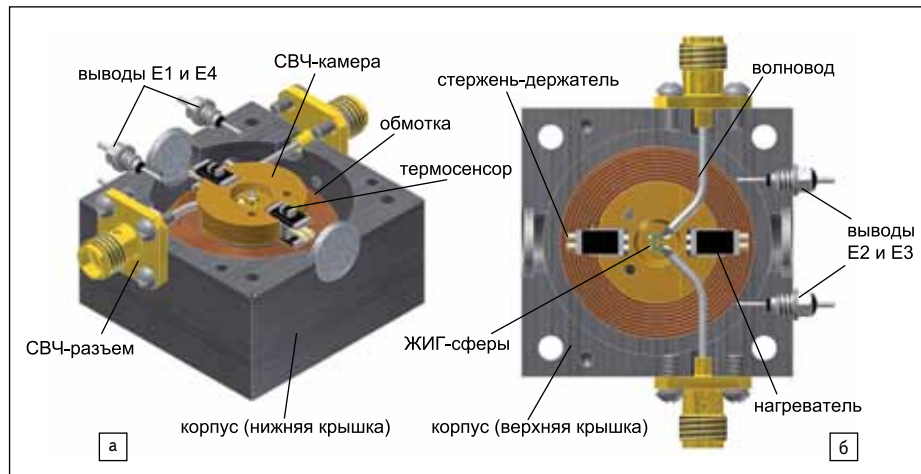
ЖИГ-фильтр: а) общий вид (без верхней крышки); б) вид снизу (без нижней крышки)
